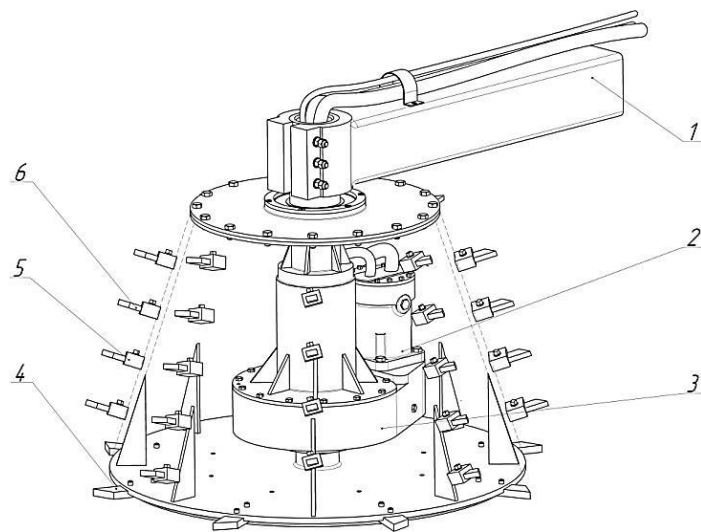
Конструкция предлагаемого рабочего органа машины для понижения пней: 1 – телескопическая стрела; 2 – гидравлический двигатель; 3 – редуктор; 4 – резец подрезной; 5 – фиксатор резца; 6 – резец скальвующий
